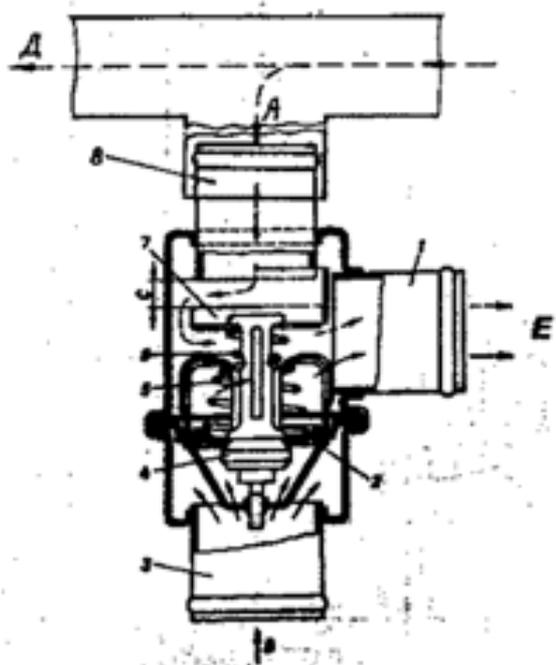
Термостат: 1 - выходной патрубок; 2 - основной клапан; 2, 3 - входной патрубок от радиатора; 4 - термочувствительный элемент; 5 - пружина основного клапана; 6 - пружина байпасного клапана; 7 - байпасный клапан; 8 - входной патрубок от двигателя; А - вход жидкости из двигателя; В - вход жидкости из радиатора; С - ход байпасного клапана; Д - к радиатору; Е - к водяному насосу
